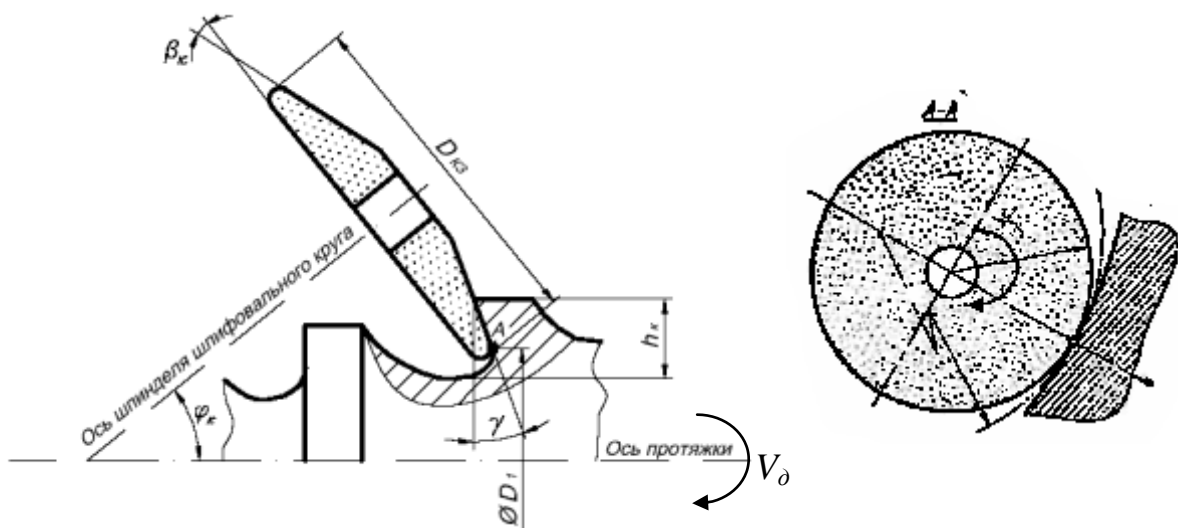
Схема загострювання протяжки по передній поверхні
